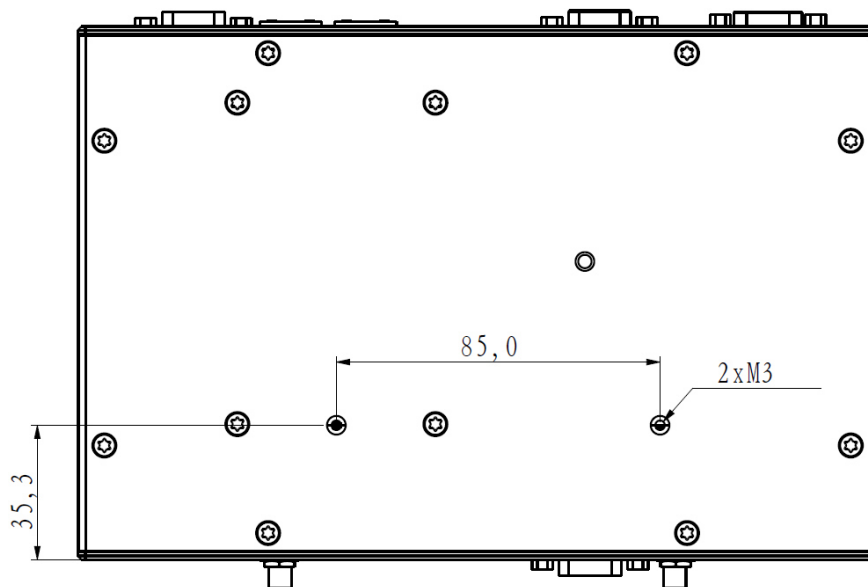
Gewindebohrungen zur Befestigung der Halterung für Hutschiennenmontage
